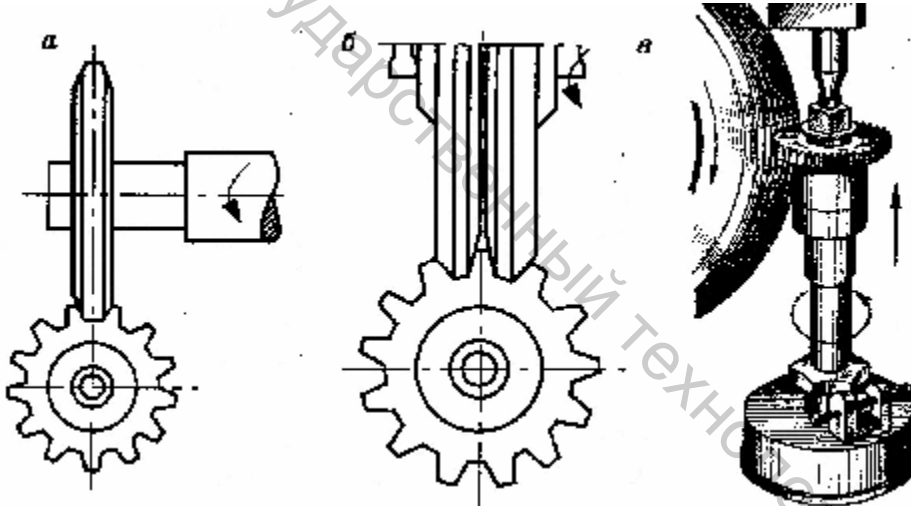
Зубошлифование цилиндрического зубчатого колеса: а — одним абразивным кругом; б — двумя абразивными кругами; в — абразивным червячным кругом
